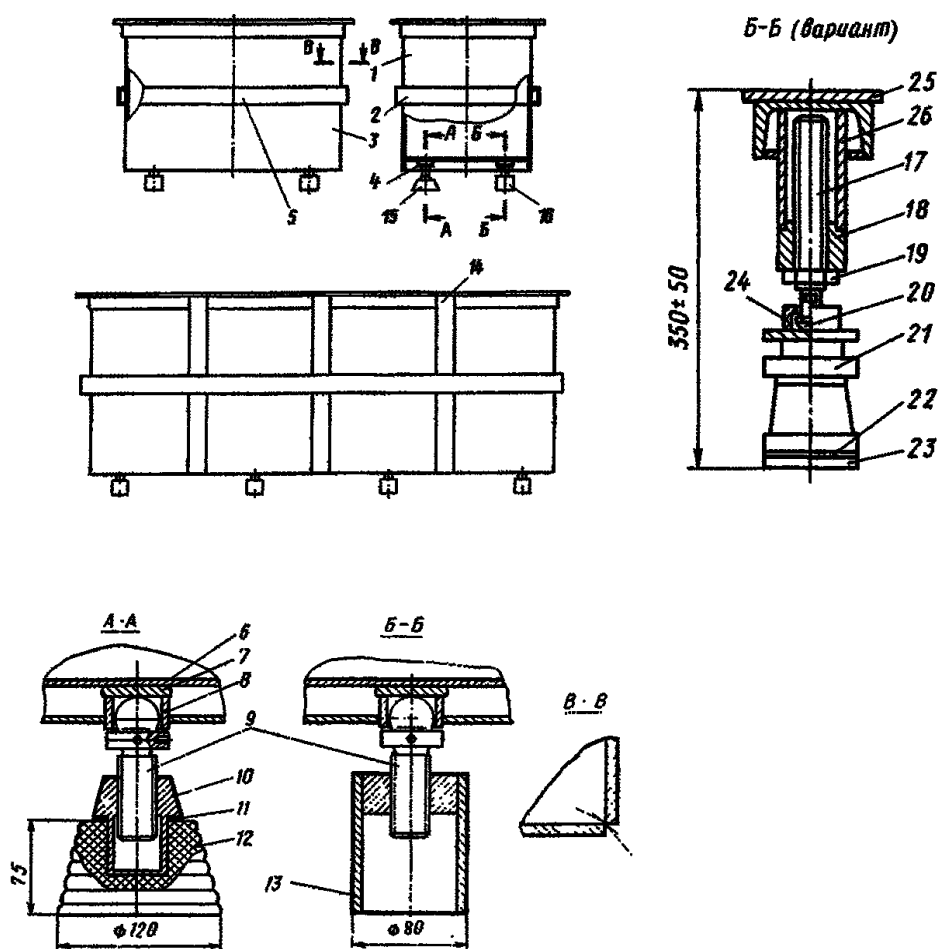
Устройство корпусов ванн: 1, 3 – боковые стенки корпуса; 2,5 – пояс из гнутого швеллера; 4 – швеллеры; 6 – дно корпуса; 7 – платина; 8 – втулка; 9 – винт; 10 – стальная втулка; 11, 22 – прокладка; 12 – фарфоровый изолятор; 13 – опора; 14 – вертикальная стойка; 15, 16 – регулируемая опора; 17 – винт грузовой; 18 – гайка; 19 – контргайка; 20 – сферический подпятник грузовой винта; 21 – изолятор фарфоровый; 23 – пята; 24 – колпачок с резьбой; 25 – дно ванны; 26 – втулка.
